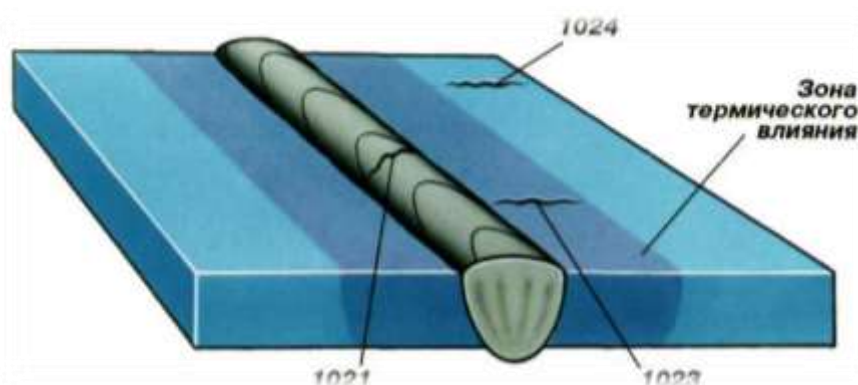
Дефекты сварного шва по типу поперечных трещин
